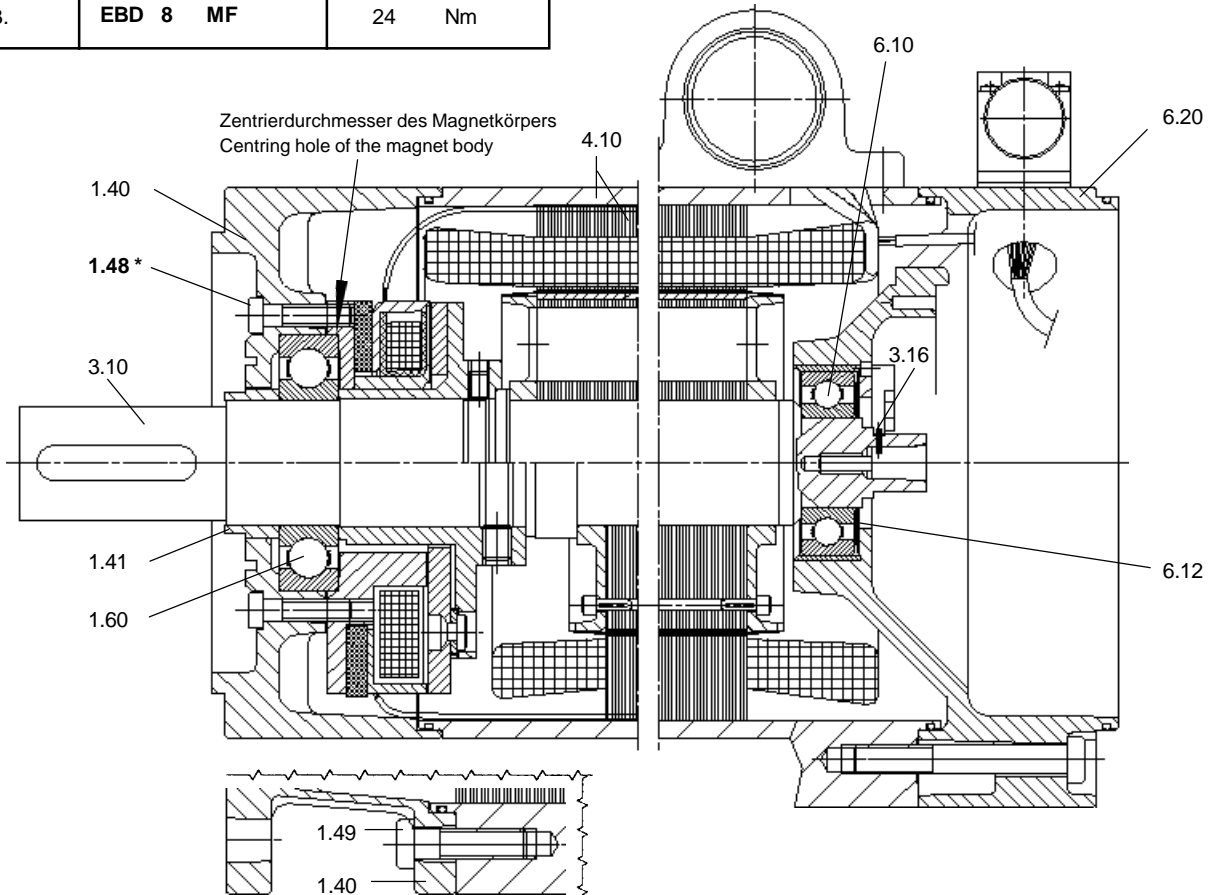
Demontage/Montage von Motorläufer / Removing/Fitting motor rotor
